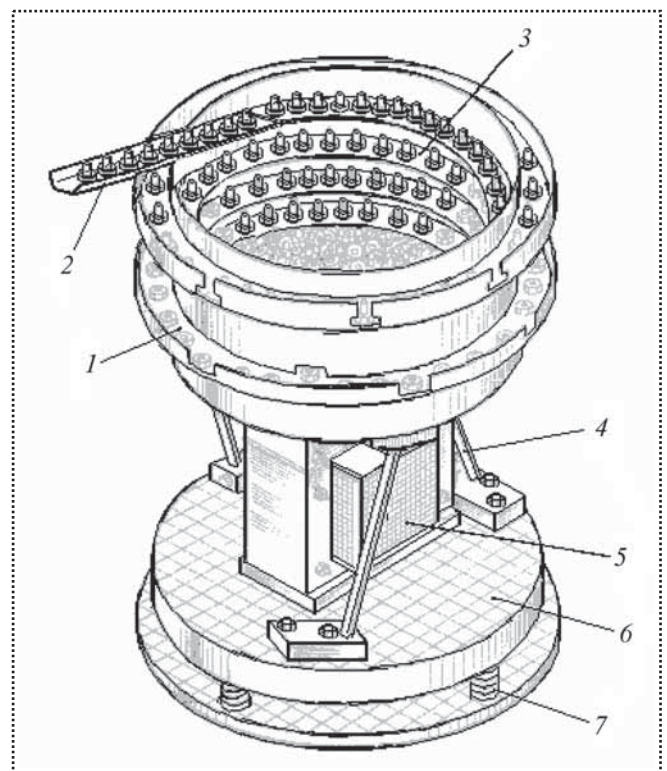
Вибробункер с одним центральным электромагнитом: 1 — наружный винтовой лоток; 2 — выходной лоток; 3 — внутренний винтовой лоток; 4 — пружина; 5 — электромагнит; 6 — основание; 7 — амортизатор
